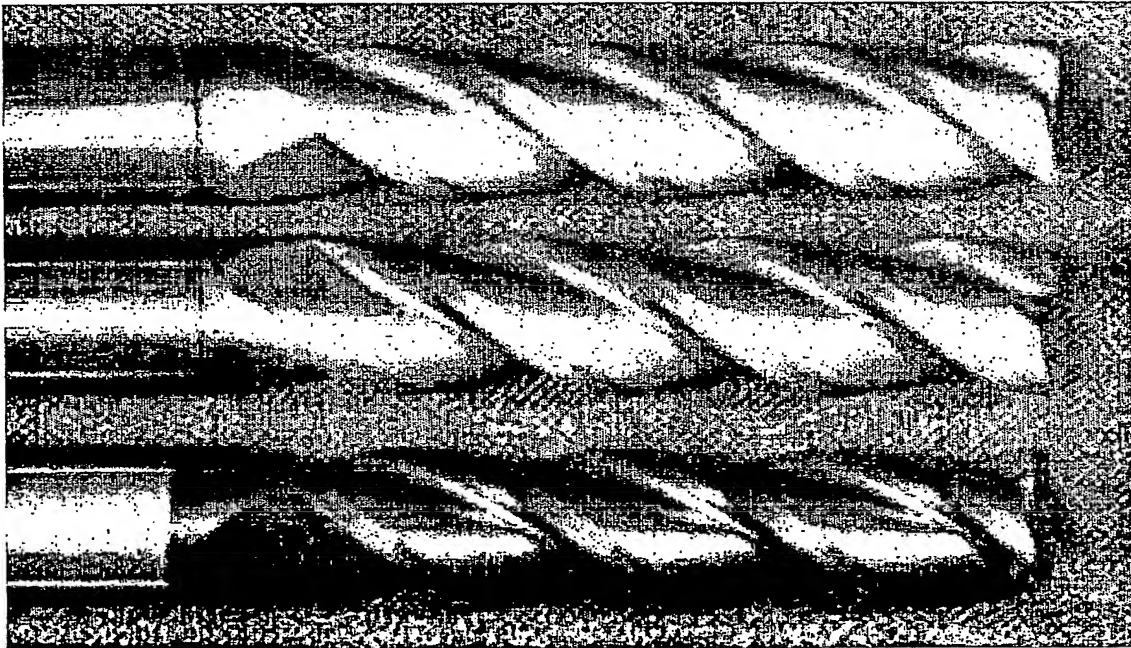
Diamantbeschichtete Fräswerkzeuge
